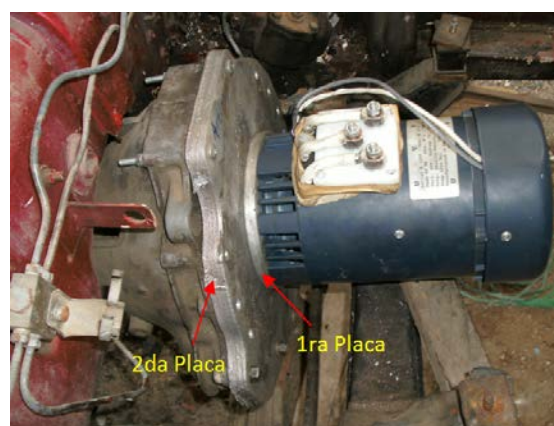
Placas de aluminio que acoplan el motor eléctrico con la caja de cambios
